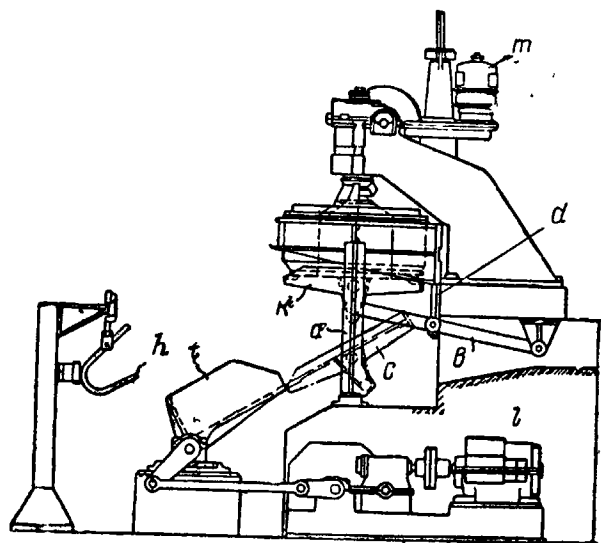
Моталка с неподвижным барабаном новой конструкции
